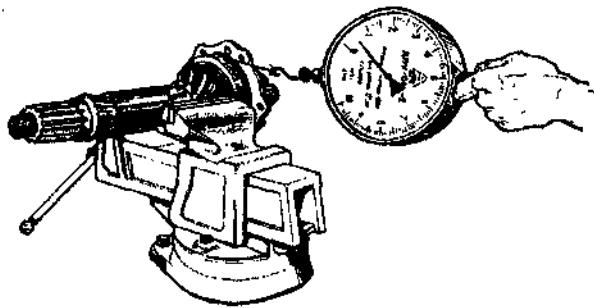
Проверка регулировки подшипников ведущей конической шестерни
